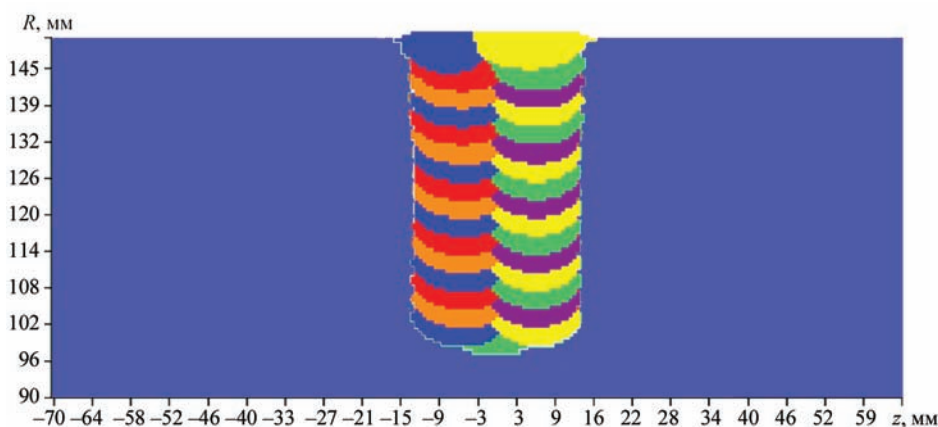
Расположение проходов при сварке кольцевого соединения (всего 33 прохода)
